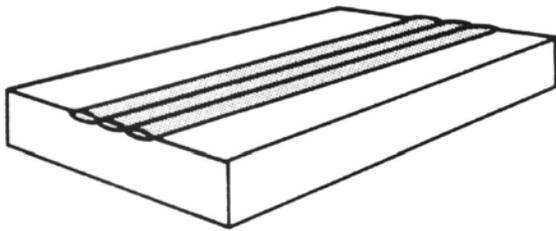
Soldaduras de Costura y Soldaduras de Puntos
